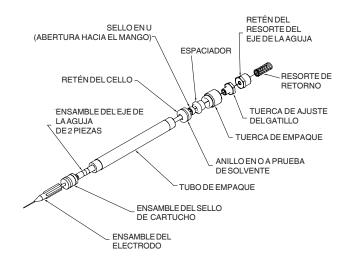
Ensamble del eje de la aguja (Empaques estándar)
